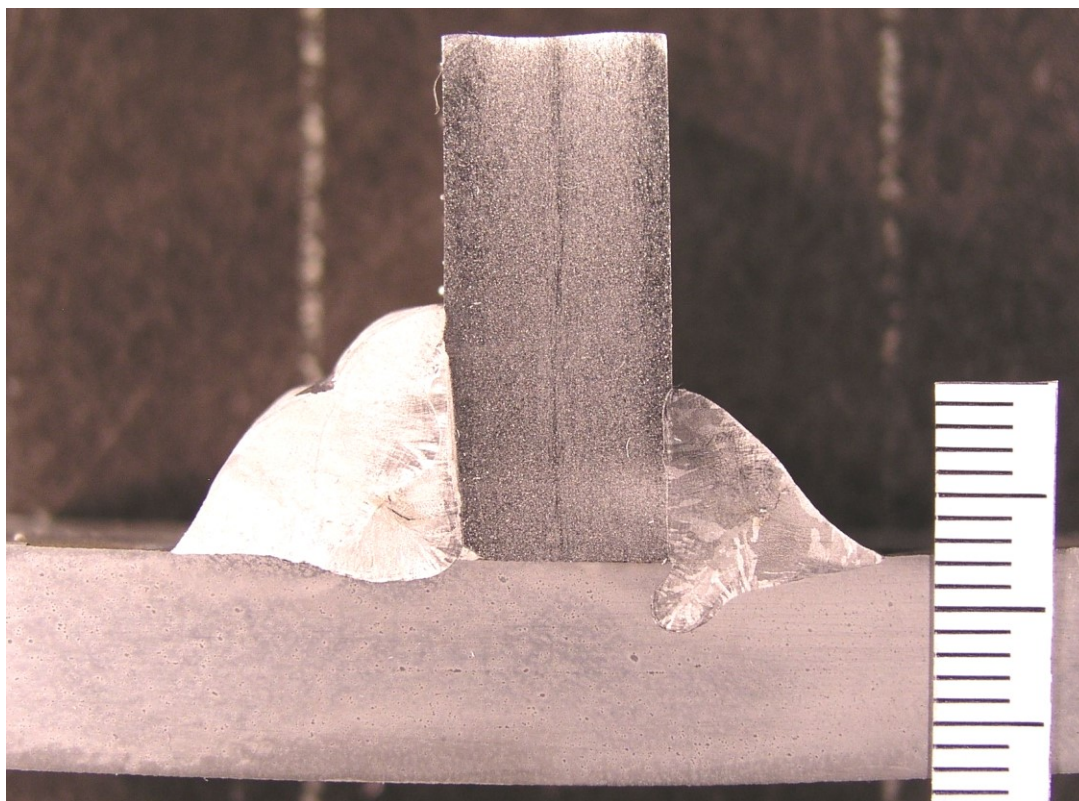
Makroizbrusak uzorka 7 - MAG-P
